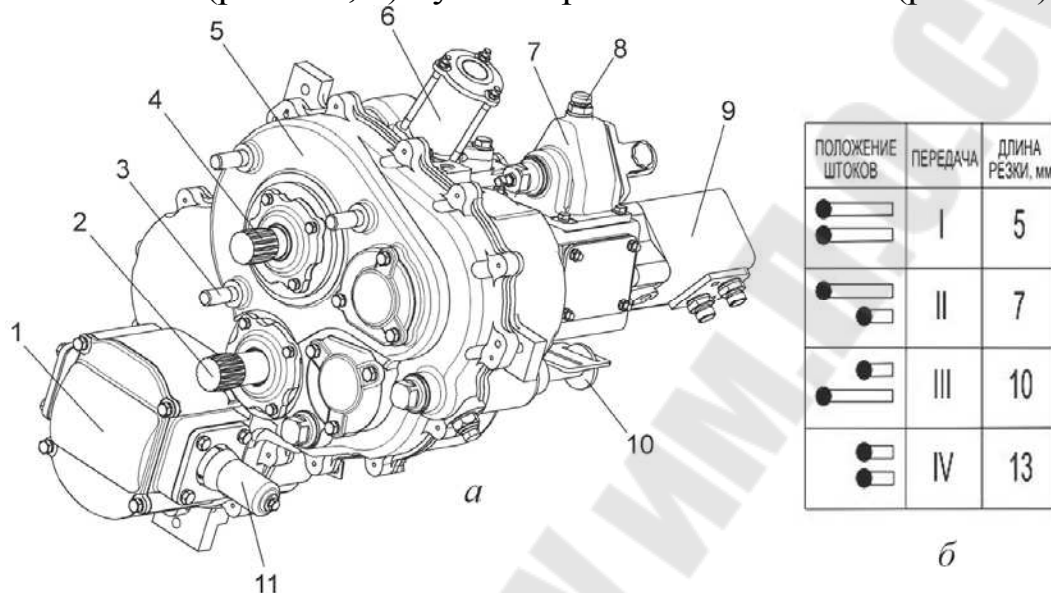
Коробка передач привода питающего аппарата (вид справа): а – привод адаптера; б – схема переключения коробки передач; 1 – крышка; 2 – вал привода коробки; 3 – шпилька; 4 – вал привода валцов; 5 – корпус; 6 – электромагнит; 7 – механизм включения реверса; 8 – сапун; 9 – гидромотор; 10 – шайба; 11 – вал привода адаптеров
